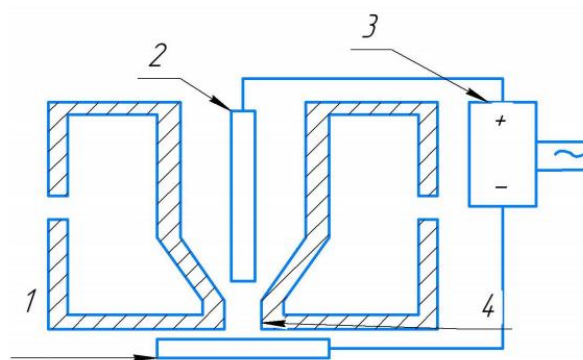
Схема зварювання на зворотній полярності W^+-Al
